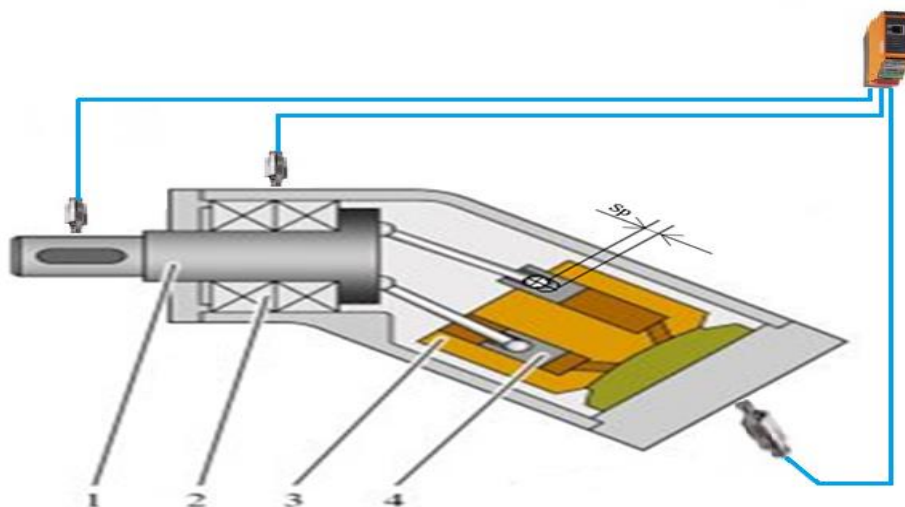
Принципиальная схема аксиально-поршневой гидромашины при дефекте в поршневой части: S_p – зазор в поршневой части; 1 – вал; 2 – подшипники; 3 – наклонный блок гидроцилиндра; 4 – поршни.
